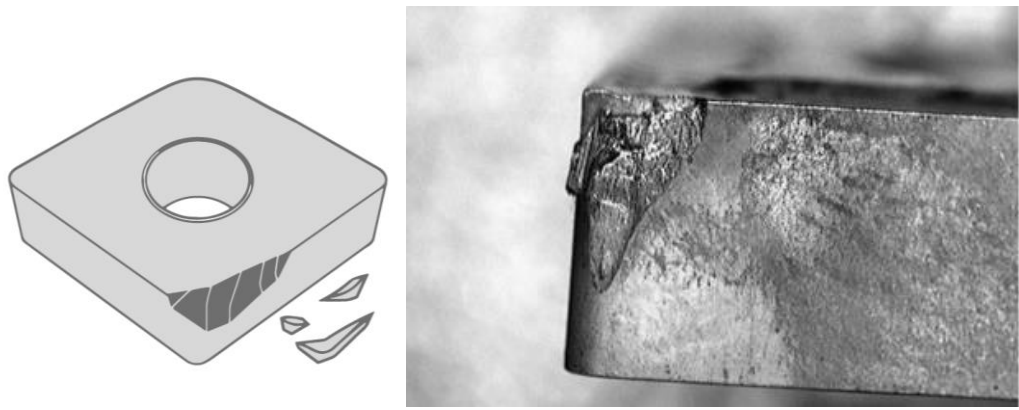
Механічне руйнування швидкоріжучої пластини
